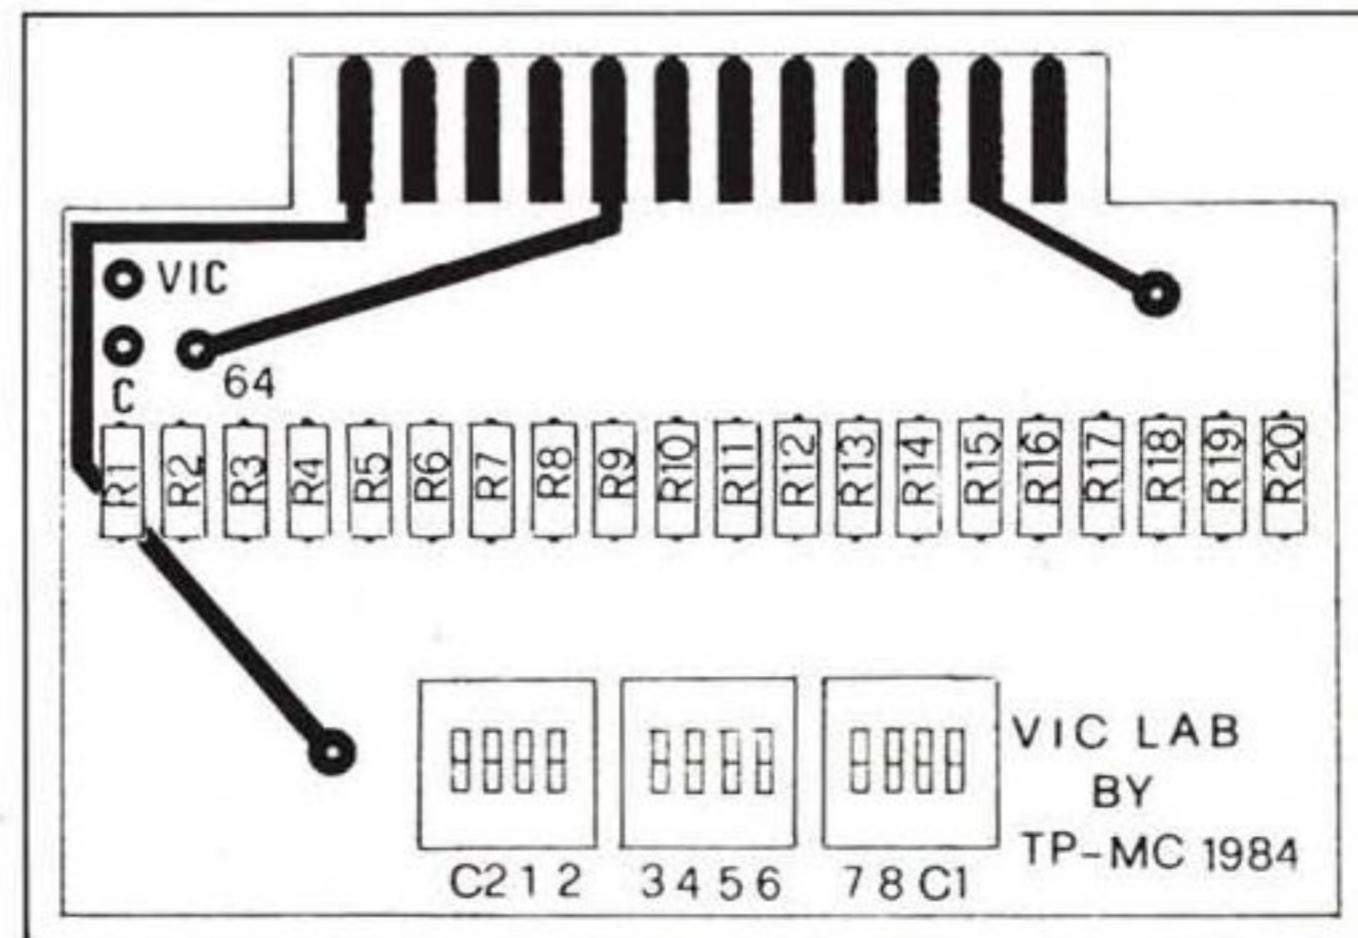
Assemblaggio dei componenti sul C.S. VL2.
